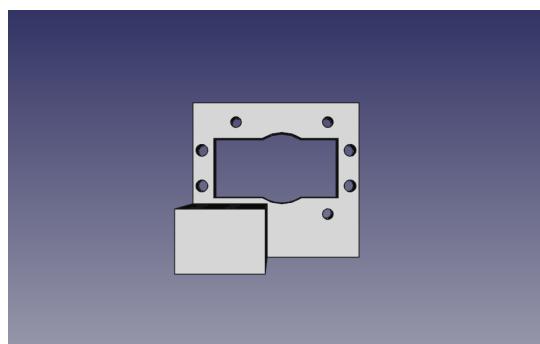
Perfil de pieza de sujeción del motor de la herramienta.
